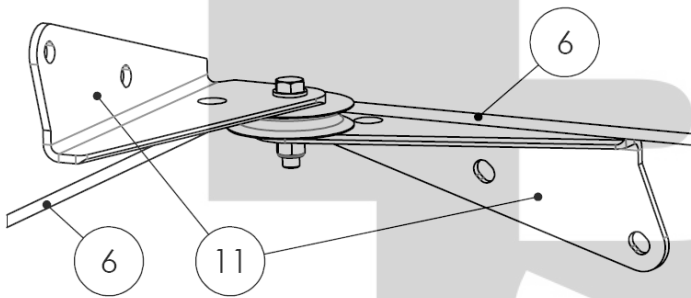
Método de montaje del cable a través de un punto de anclaje de esquina interior.
